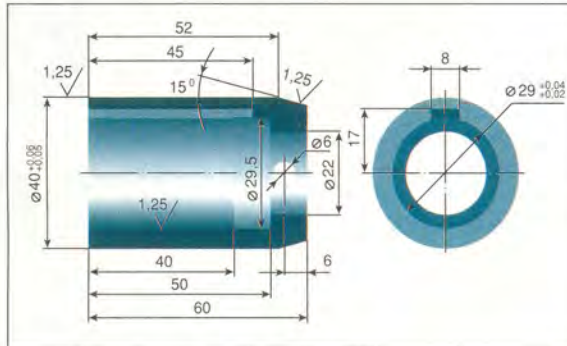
Оправка для установки крышки привода распределительного вала с сальником двигателей ВАЗ–2101, –2103, –2106 (центрирование по коленчатому валу).
